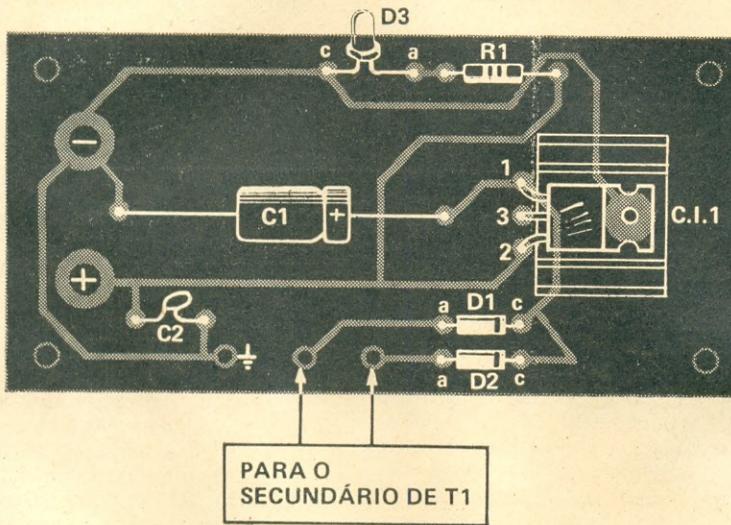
Disposição dos componentes sobre a plaqueta da Fig. 2. Somente o transformador T1 ficou fora da plaqueta.
